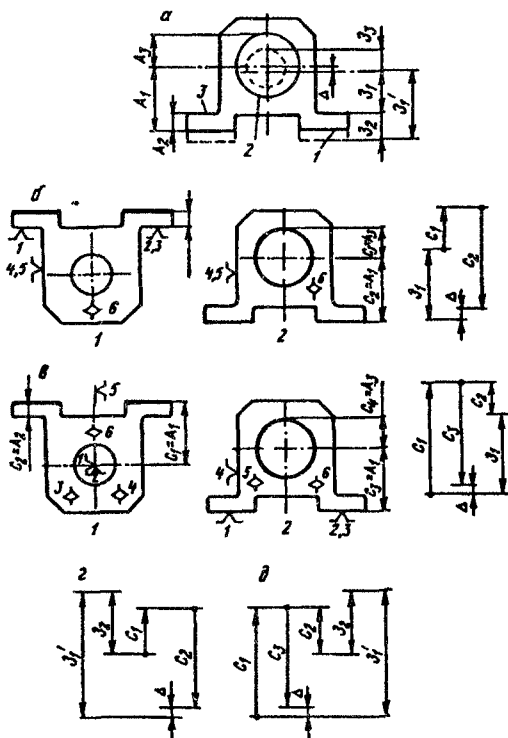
Пример выбора базы для первой операции обработки заготовки корпусной детали
